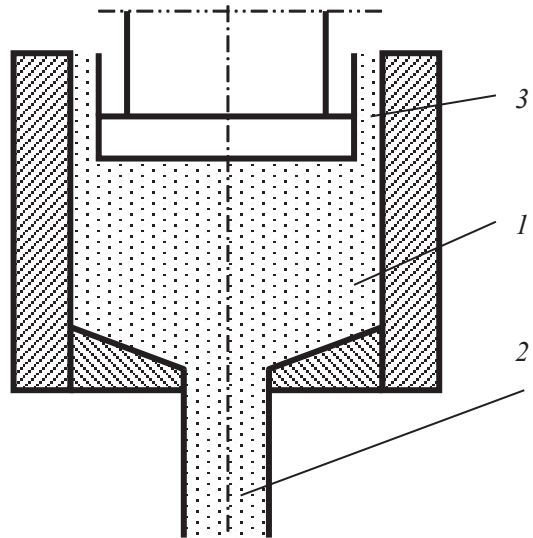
Схема прессования с рубашкой: 1 — слиток; 2 — пруток; 3 — рубашка
